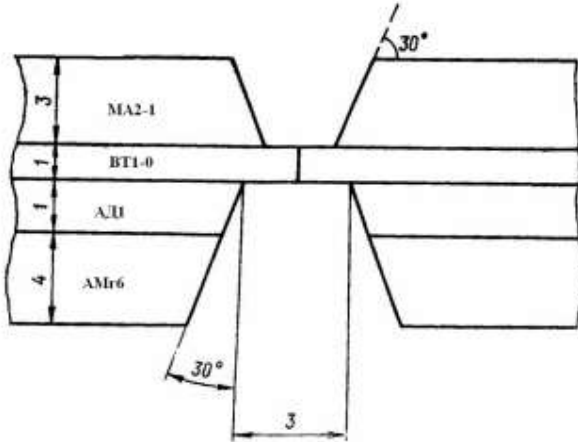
Схема підготовки кромок до зварювання багатошарового матеріалу
